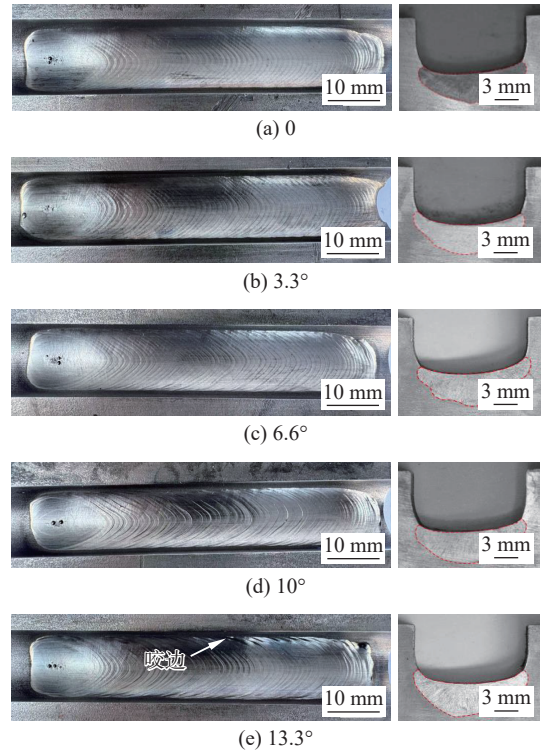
不同摆动角度焊缝表面成形及截面形貌
